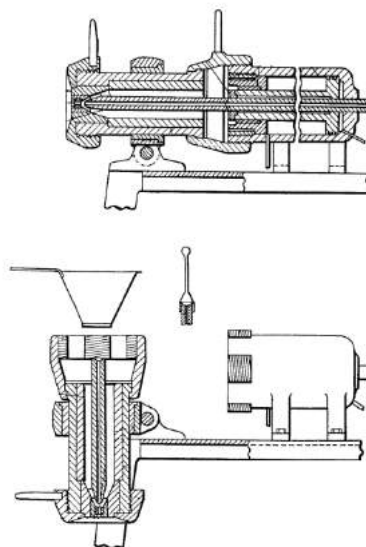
diseño de extrusora hidráulica. Fuente: wespec.net
